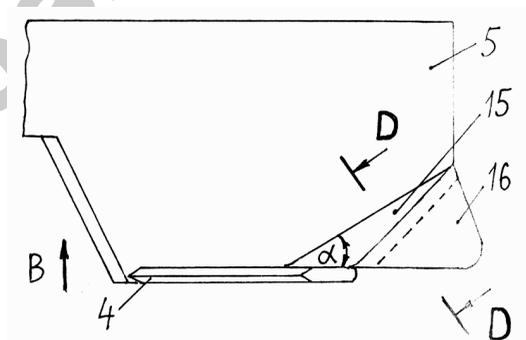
Уплотнитель свода дрены (вид сверху)
